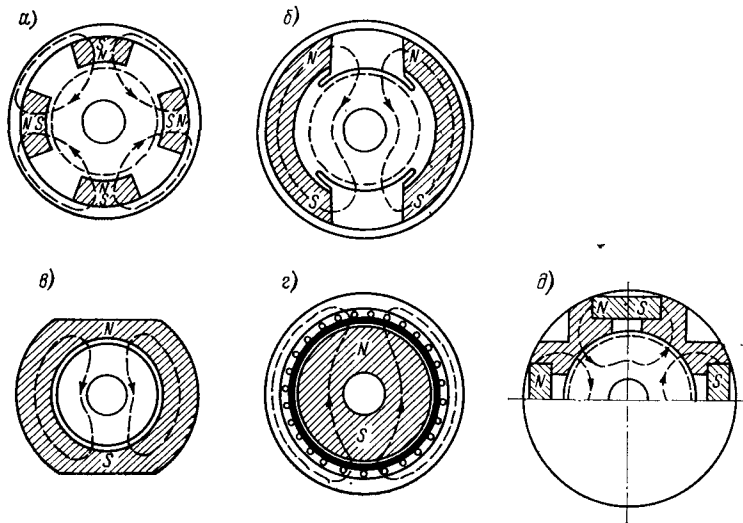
Конструкция магнитных систем двигателей с постоянными магнитами: а — радиальные магниты; б — скобообразные магниты; в — кольцевой магнит; г — внутренний цилиндрический магнит; д — плоские магниты с полюсными наконечниками
